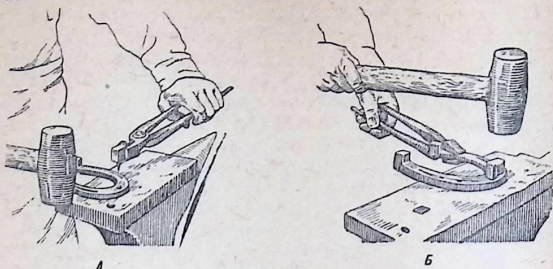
Укрепление зацепного шипа для сварки:
